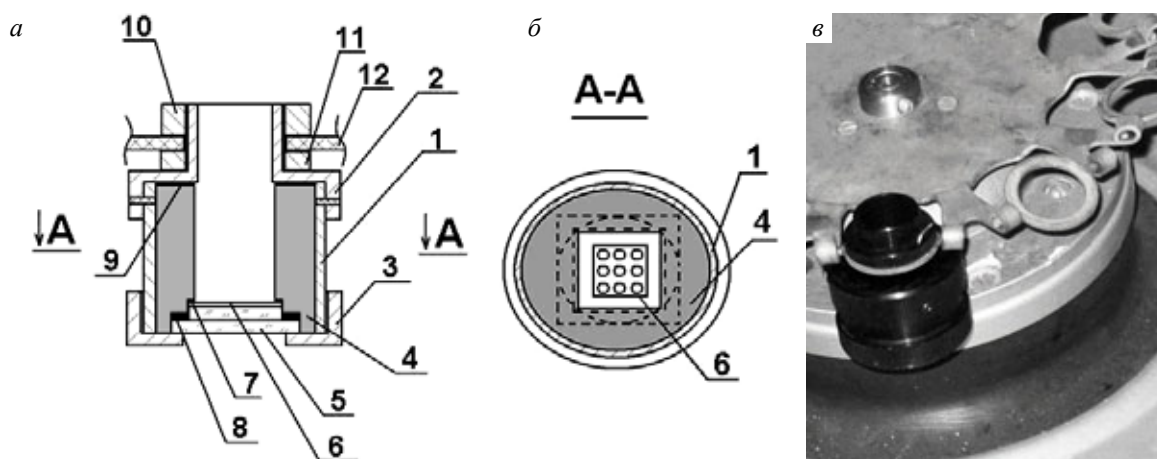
Приспособление для осаждения клеток на поверхность биочипа путем центрифугирования: а — вид сбоку в разрезе; б — вид сверху в разрезе; в — приспособление, закрепленное на роторе центрифуги ОПН-3; 1 — центральная секция корпуса; 2 — верхняя секция корпуса; 3 — нижняя (прижимающая) съемная секция корпуса; 4 — съемная вставка; 5 — дно; 6 — биочип; 7, 8, 9 — герметизирующие эластичные прокладки; 10 — крепление; 11 — съемное кольцо; 12 — ротор центрифуги
